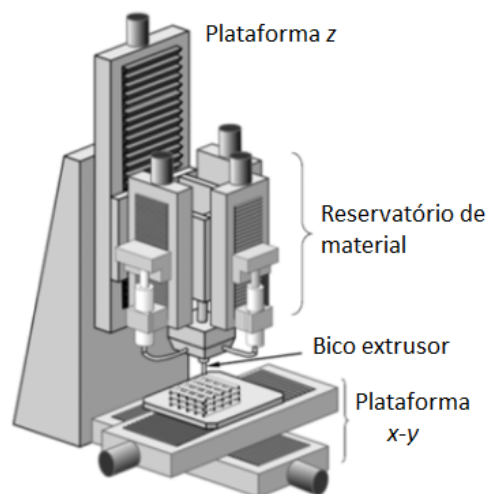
Desenho esquemático do processo Robocasting [34].
